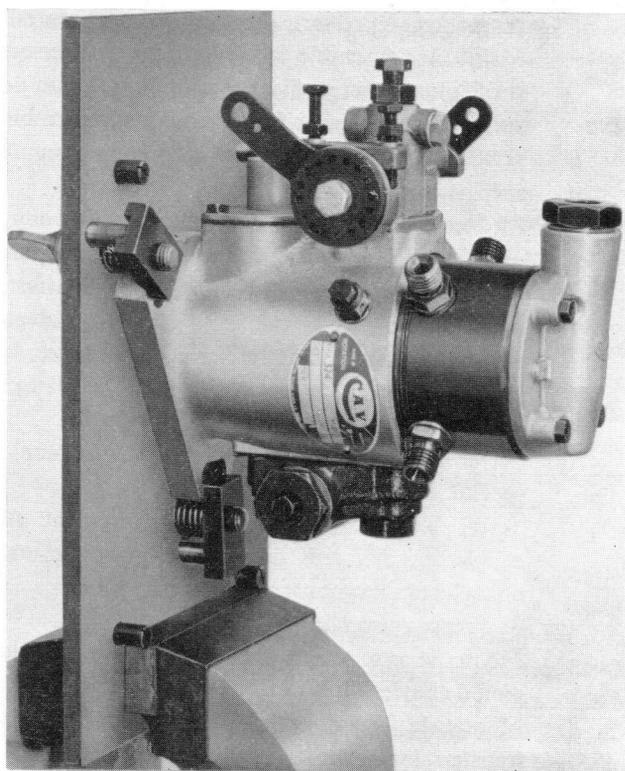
Régulateur hydraulique à montage réversible fixé sur la plaque de démontage et de remontage
